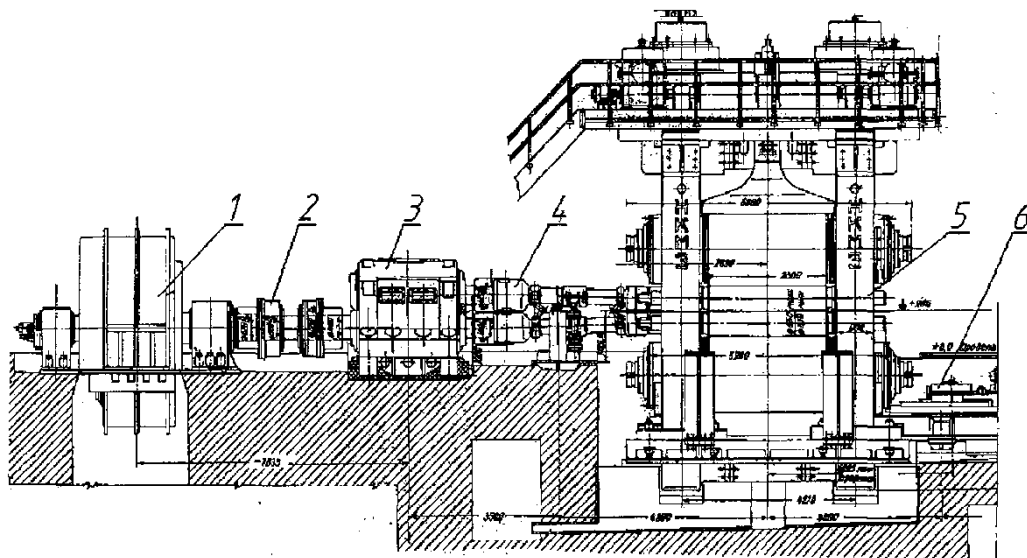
Главная линия стана 2000 горячей прокатки: 1- электродвигатель; 2 - зубчатая муфта; 3 - шестеренная клеть; 4 - универсальный шпиндель; 5 - рабочая клеть; 6 - тележка для перевалки валков
